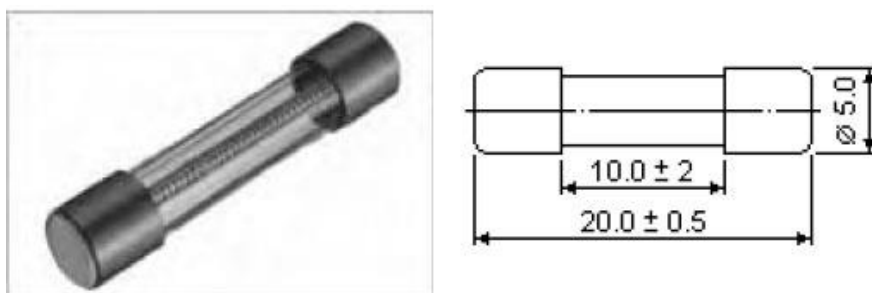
Зовнішній вигляд і габаритні розміри запобіжника ZH214-015 10A-250 В
